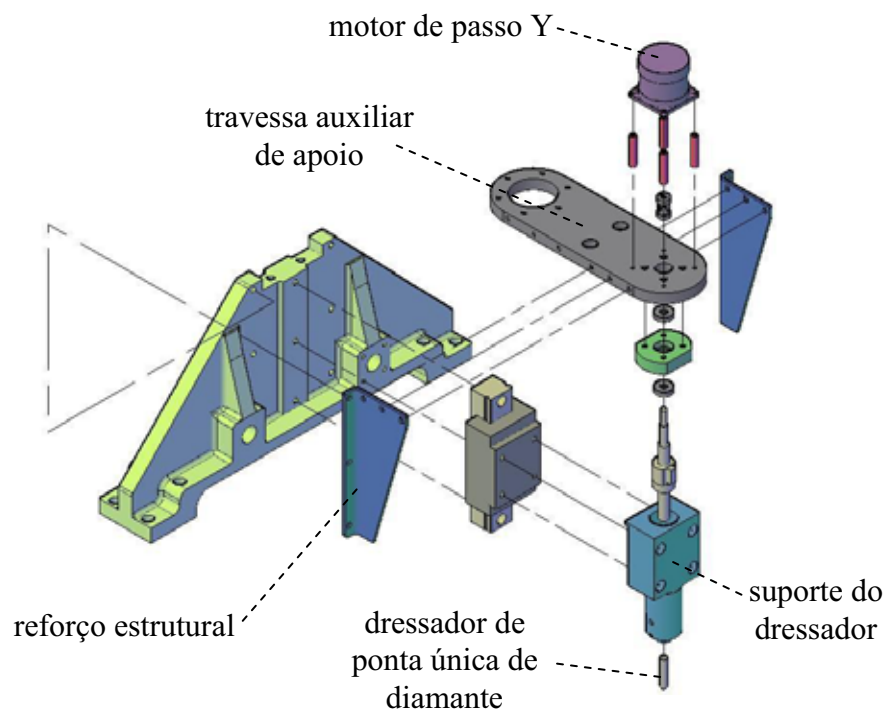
Perspectiva explodida dos principais constituintes mecânicos responsáveis pelo movimento, perpendicular à superfície do rebolo, do dressador.
